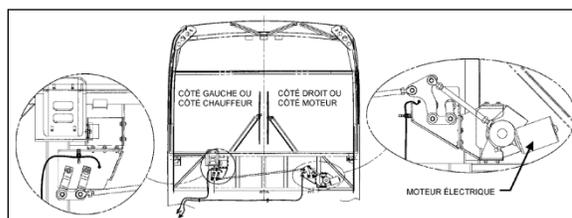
INSTALLATION DES ESSUIE-GLACES 23287
